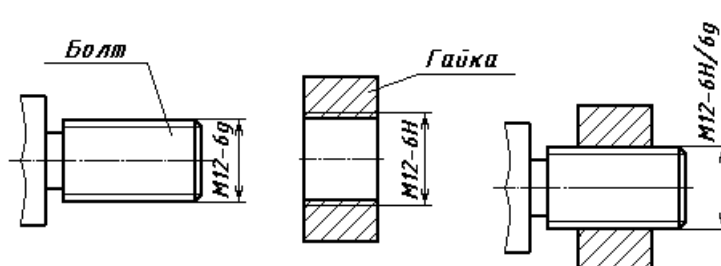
Обозначение метрической резьбы на чертежах
